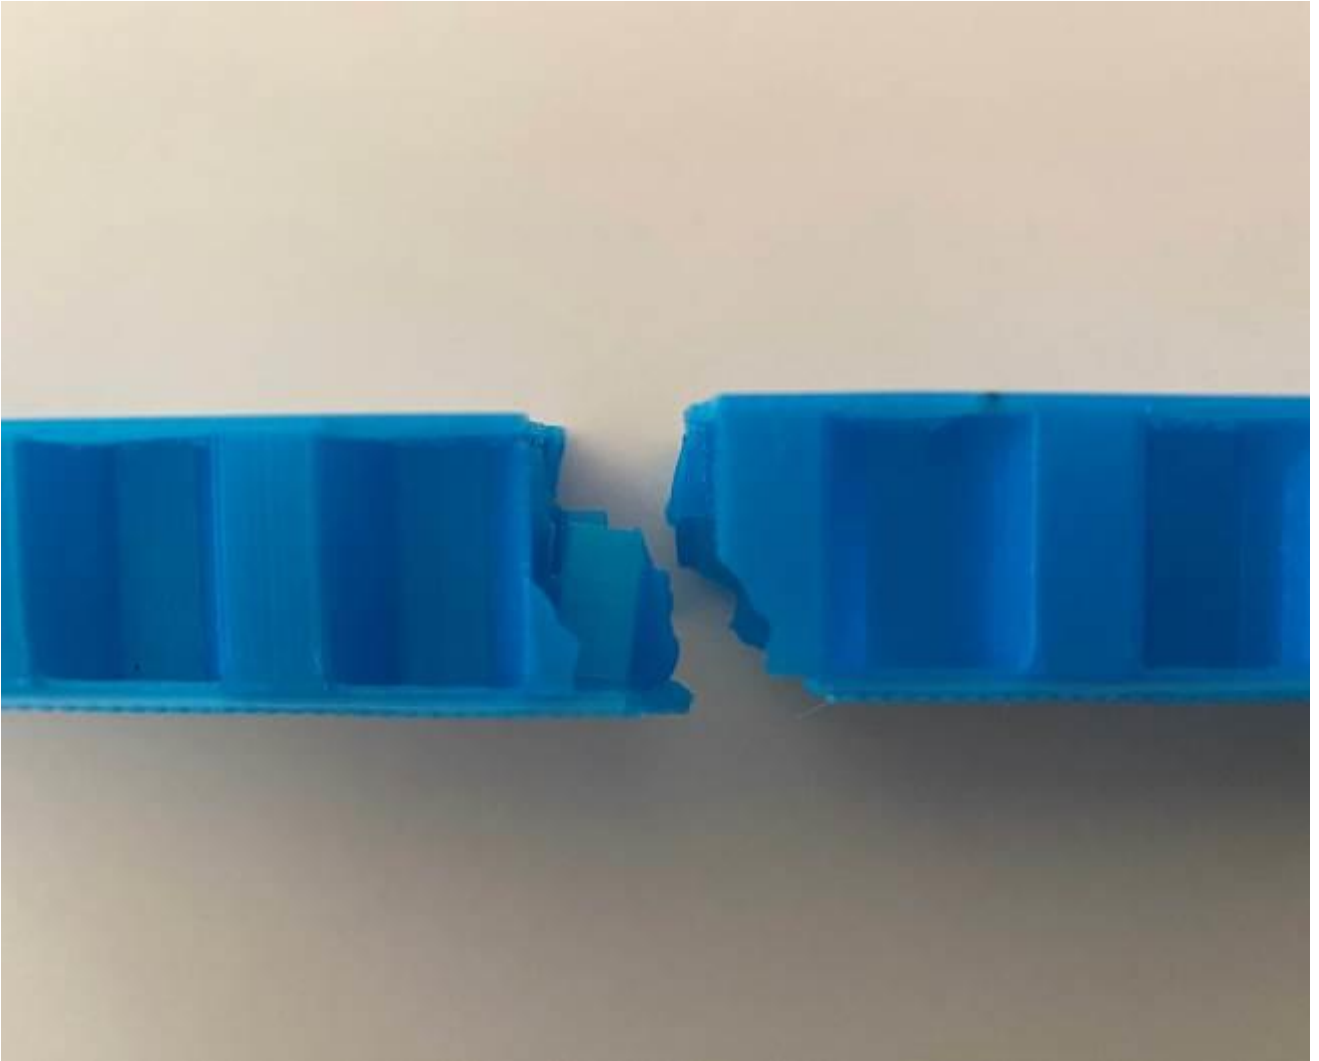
Espécimen 6 del lote de 3/8" fabricado completamente en PLA con tratamiento térmico, tipo de falla X-A-F.
